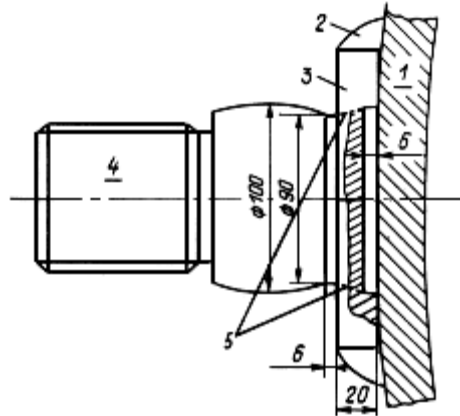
Повреждение узла подвески крышки: 1 - крышка; 2 - сварной шов приварки крышки; 3 - подошва оси; 4 - ось подвески крышки; 5 - линия разрушения узла
